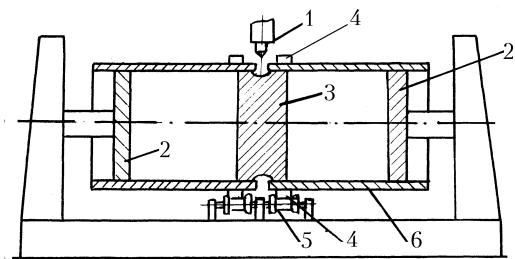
Зварювання обичайок у стапелі токарного типу:
